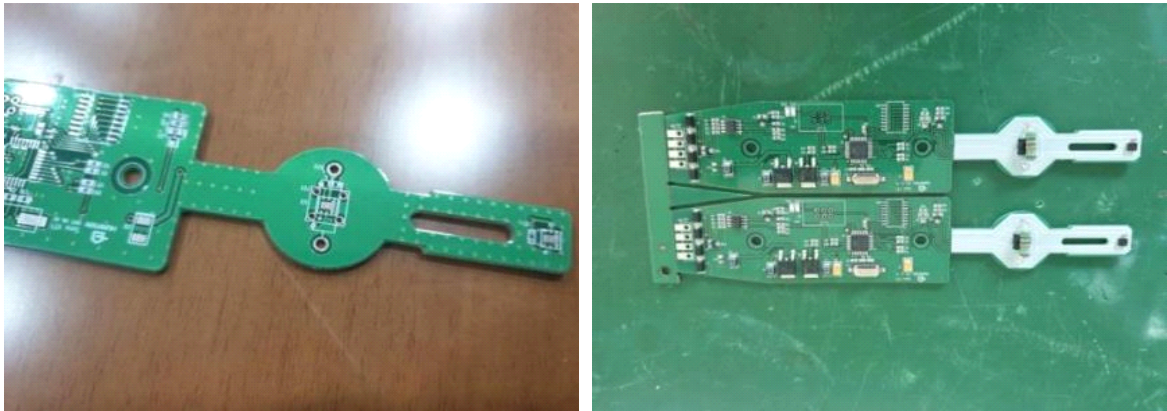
개별 온습도 센서 PCB 설계 및 제작 (2)
